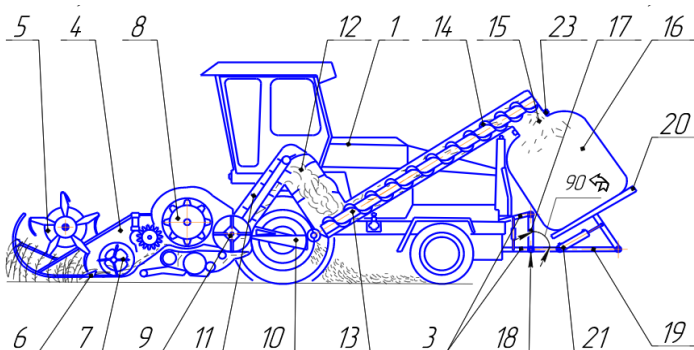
Машина полевая для заготовки и сбора зернового вороха
